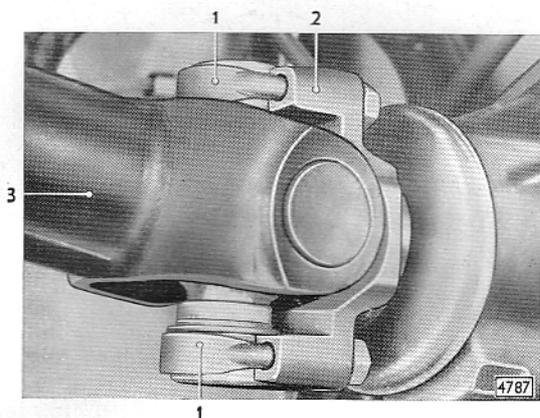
Gelenkwelle am Antriebskegelradflansch befestigt
